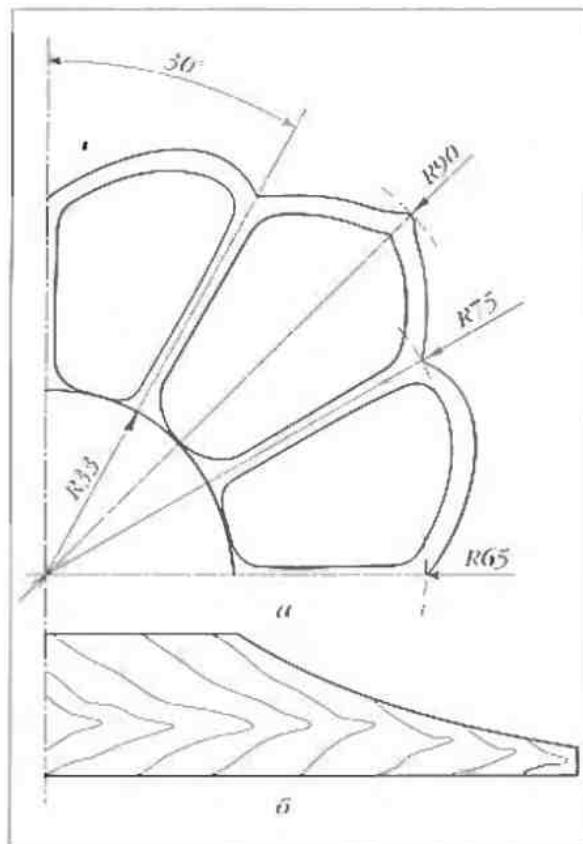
Шаблон основания вазы (масштаб 0,85:1): а – вид в плане; б – сечение заготовки
